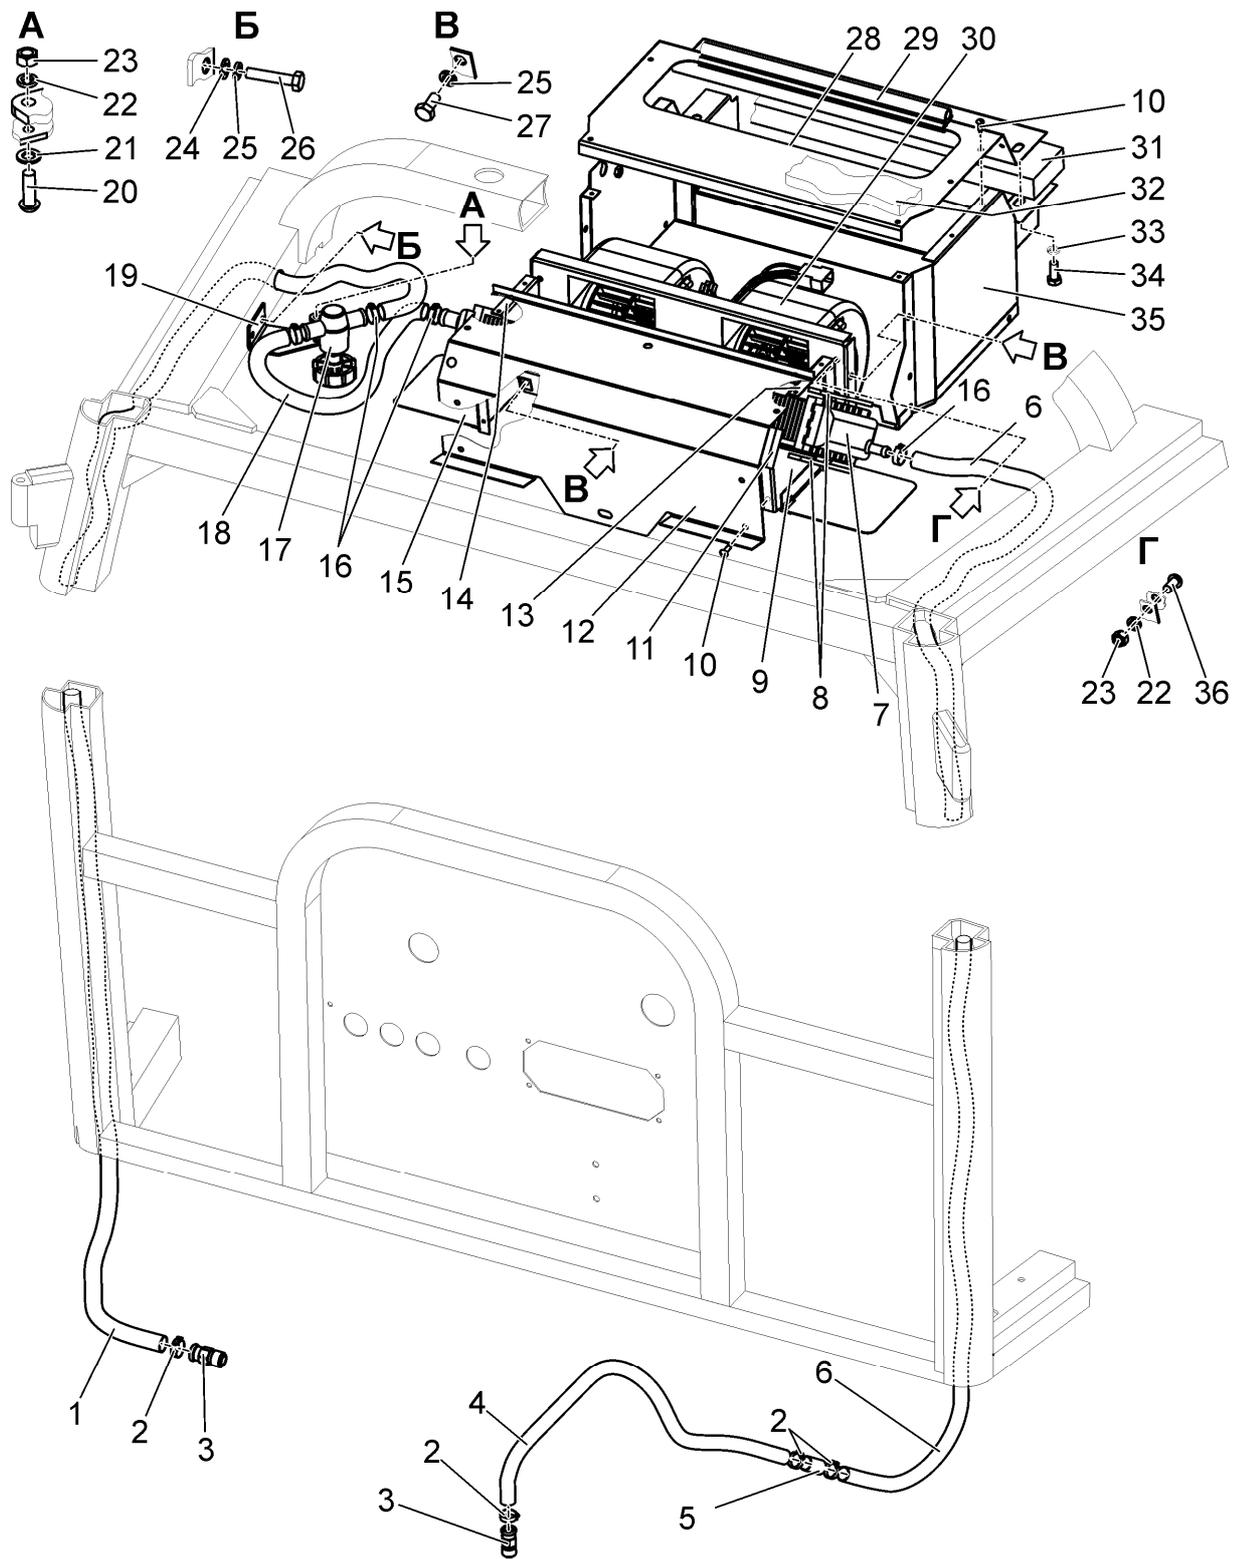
Система отопления и вентиляции. Арматура отопителя.
